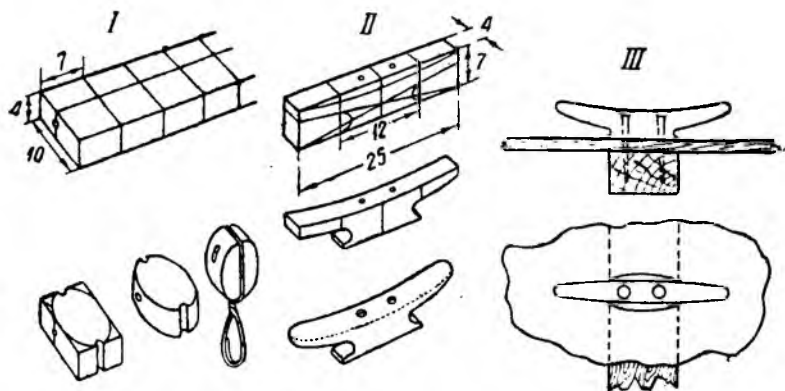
Деревянные утка и блок: I — изготовление блока; II — изготовление утки; III — крепление утки к палубе.
